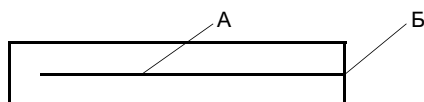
Образец для сварки (А — рез, Б — прижим)
